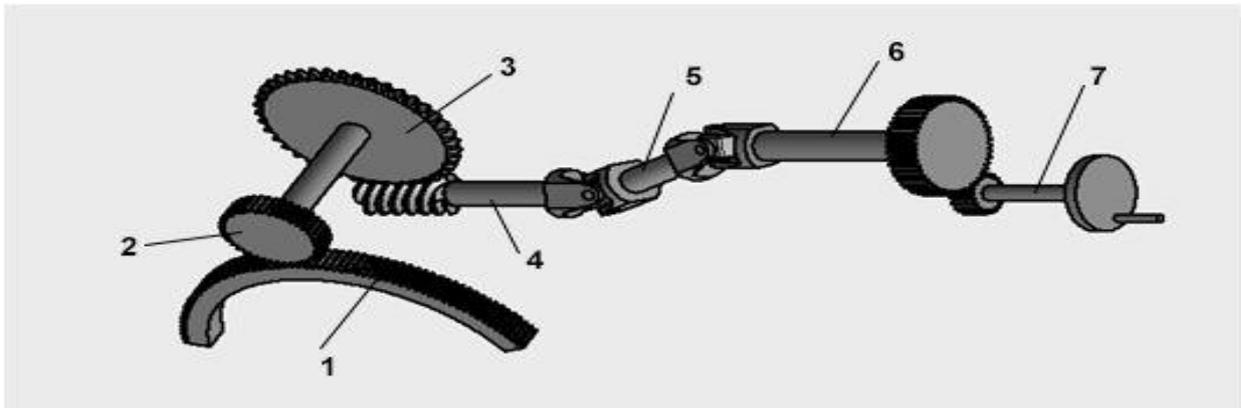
Загальний вигляд механізму: 1 – зубчатий сектор; 2 – шестерня; 3 – черв’ячне колесо; 4 – черв’як; 5 – шарнір; 6 – вал з шестернею; 7 – маховик;
